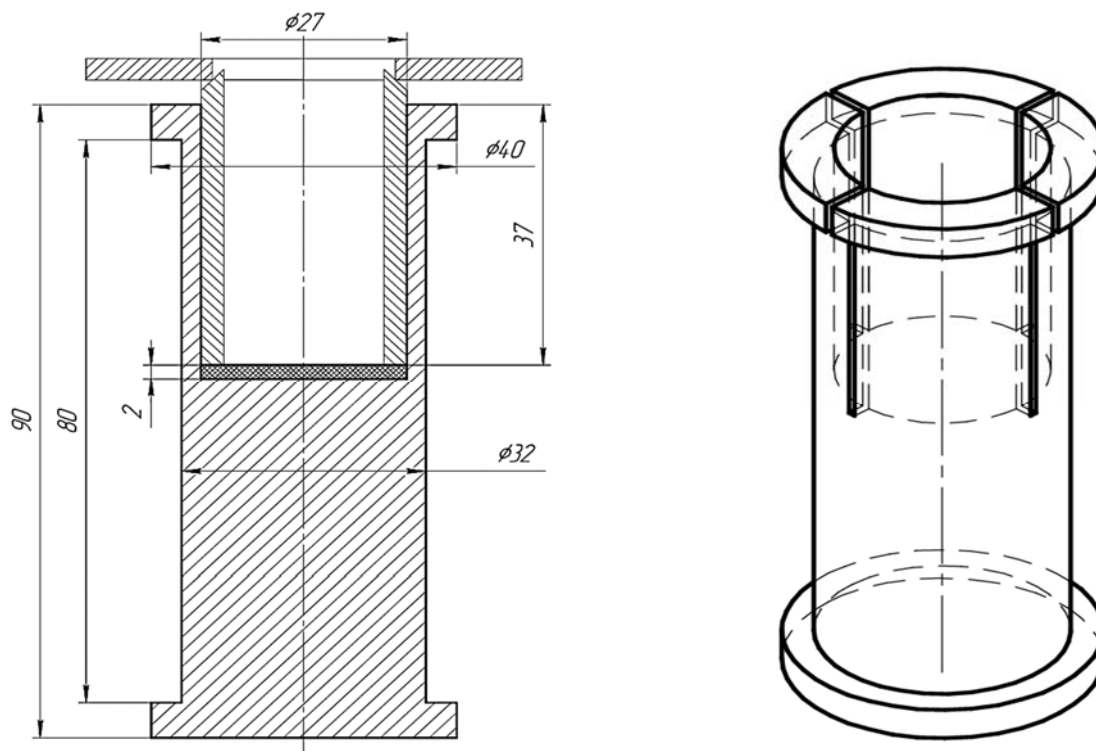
Электрод цангового типа для бокового токоподвода к цилиндрической поверхности втулки
